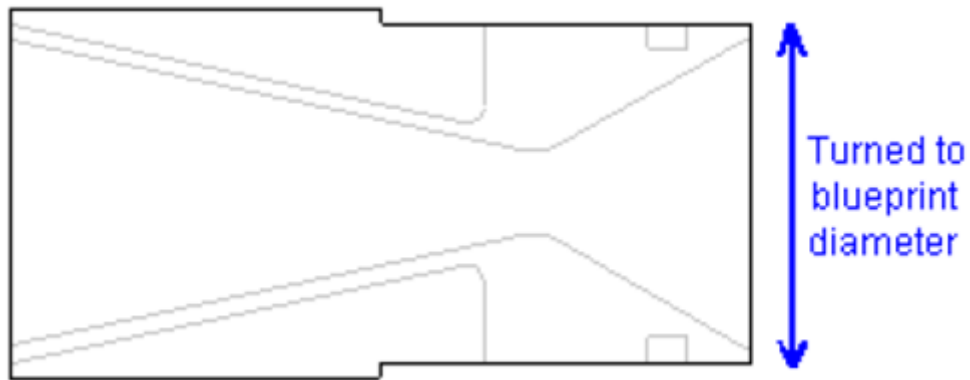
Cilindrado de la parte de la tobera que penetra en la cubierta del motor
